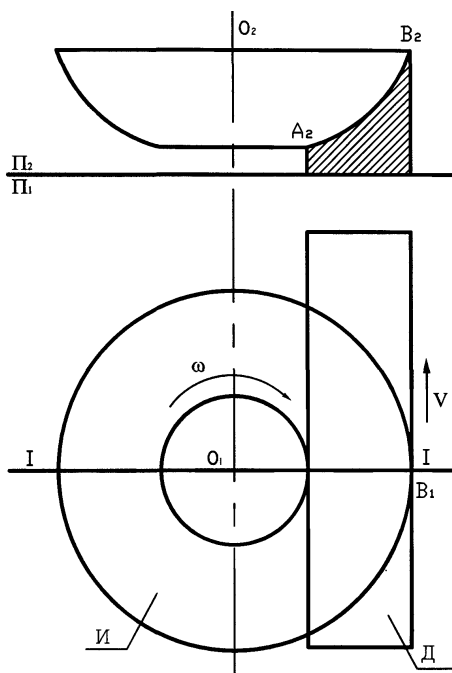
Схема фрезерування фасонних циліндричних поверхнь торцевими фрезами
